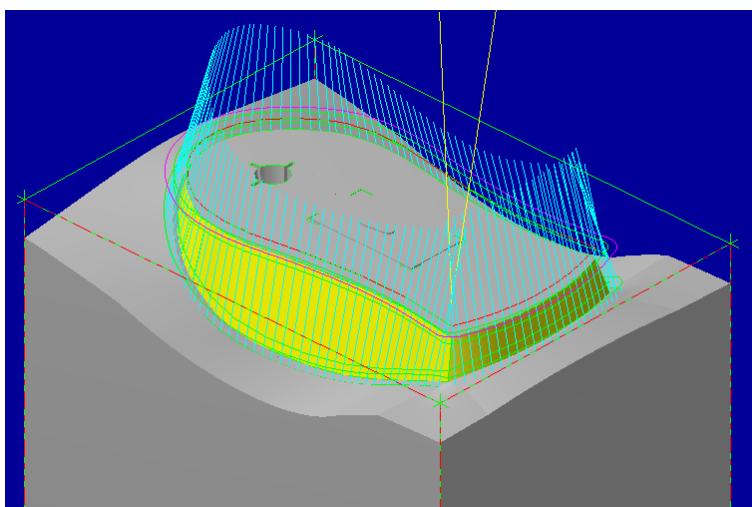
Toolpath criado para maquinagem das faces laterais do rato.
